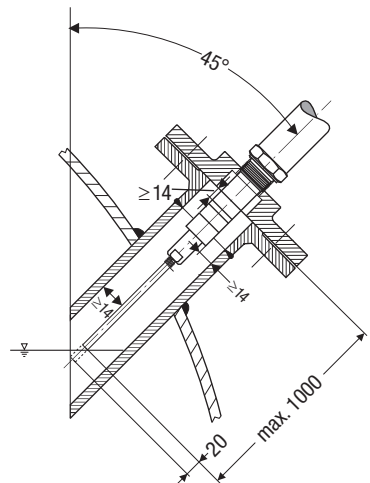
Schrägeinbau z.B. in Dampfkesseln
